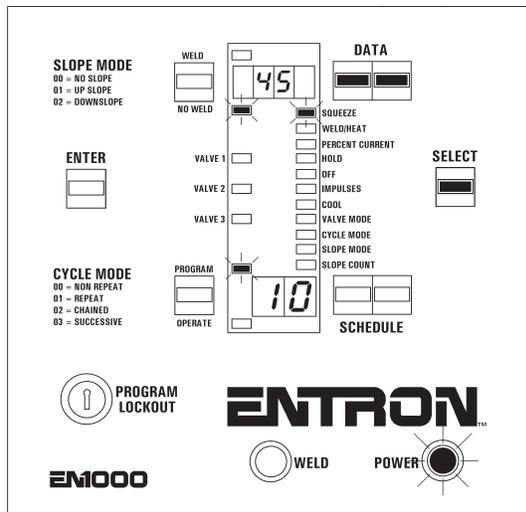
Ponga el control en NO SOLDAR (NO WELD)
